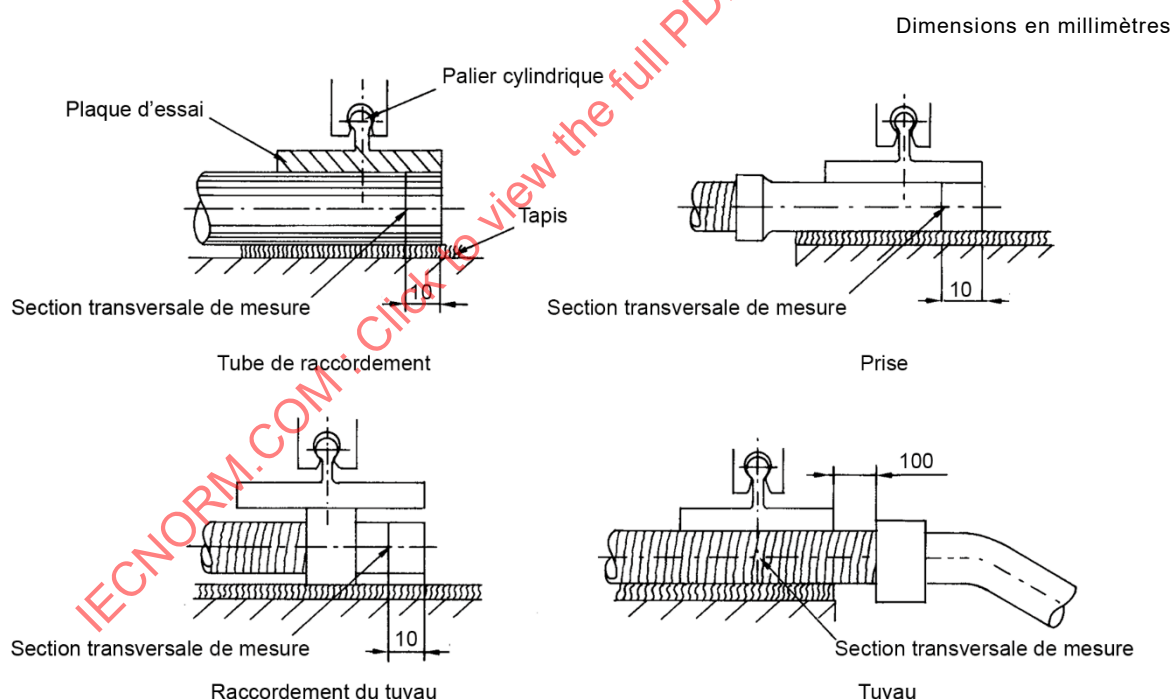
Position de l'objet d'essai et section transversale de mesure de la déformation
